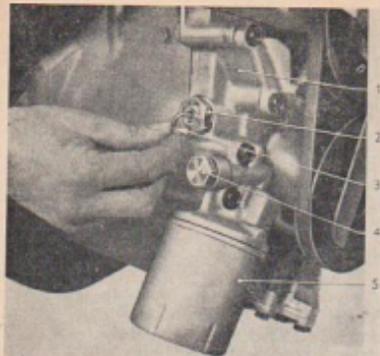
Arretierten Öldruckkolben für Kettenspanner entspannen
